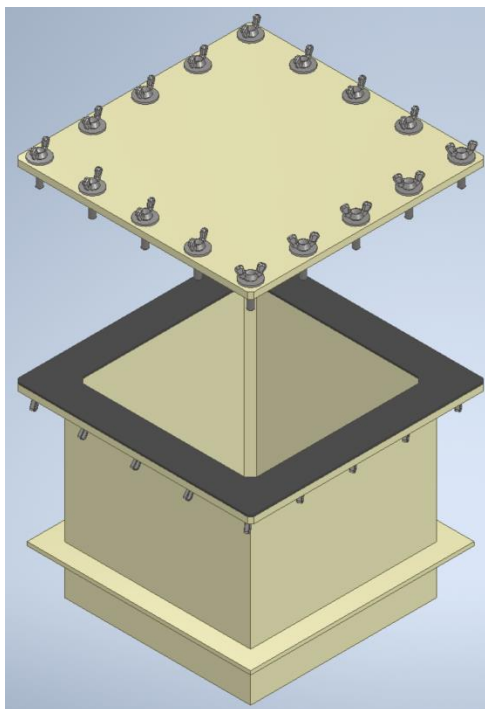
Tampa de acesso em chapa de PEAD ou Polipropileno, com junta de vedação prensada entre flanges.
